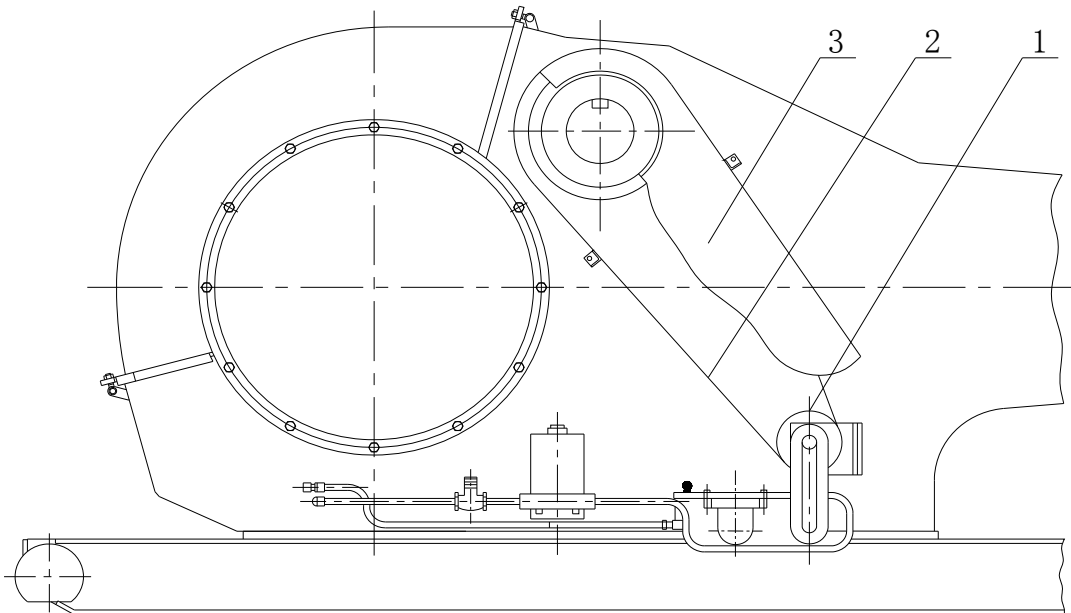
Короткий чертёж «установка масляного насоса внутри корпуса»
